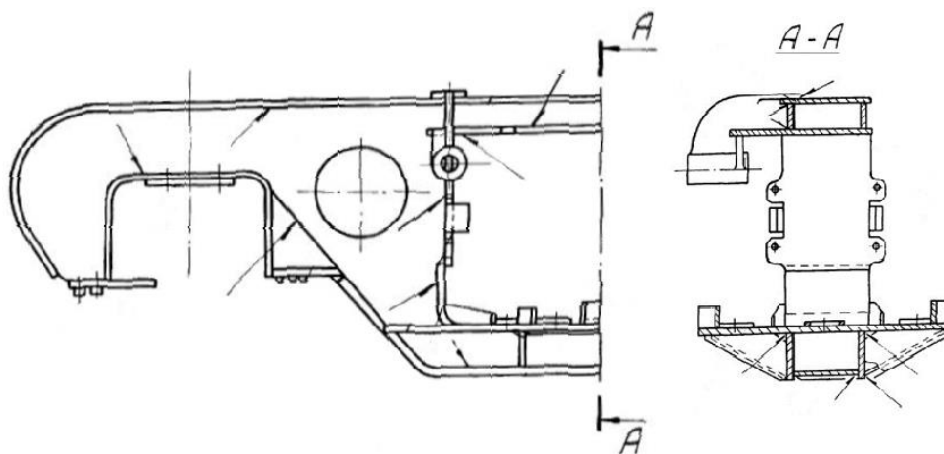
Зварна конструкція бокової рами візка, розробник КВБЗ
